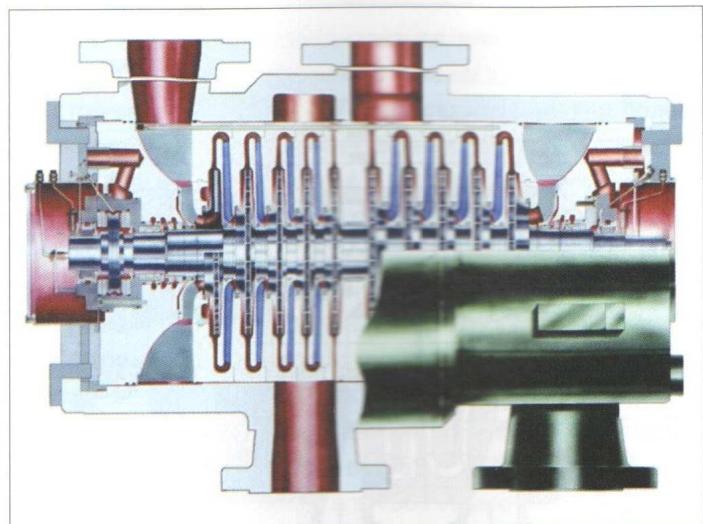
Корпус сжатия компрессора высокого давления с вертикальным разъемом
